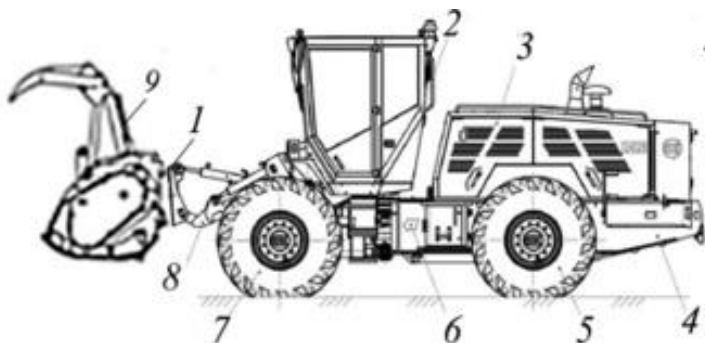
Общий вид мульчера: 1 – адаптер; 2 – кабина; 3 – установка силовая; 4 – рама; 5, 7 – ведущие мосты с колесами; 6 – коробка раздаточная; 8 – стрела.
